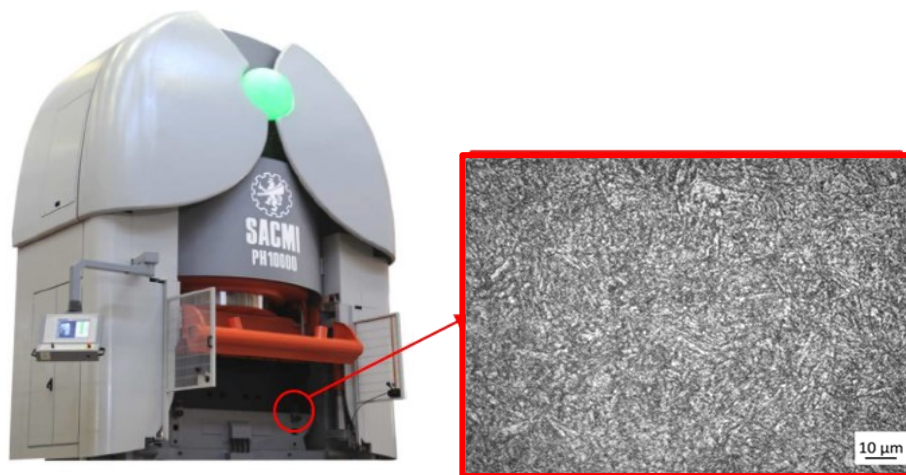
Presse SACMI; struttura dell'acciaio da stampi
